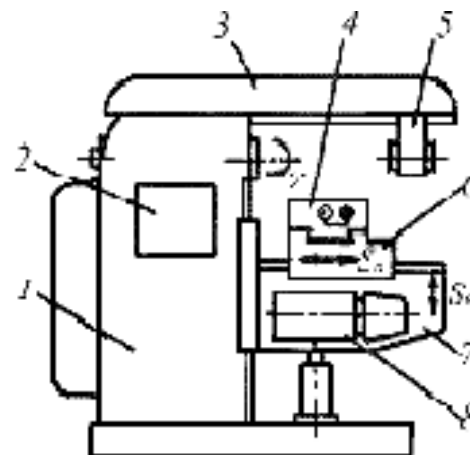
Загальний вигляд горизонтально-фрезерного верстата
